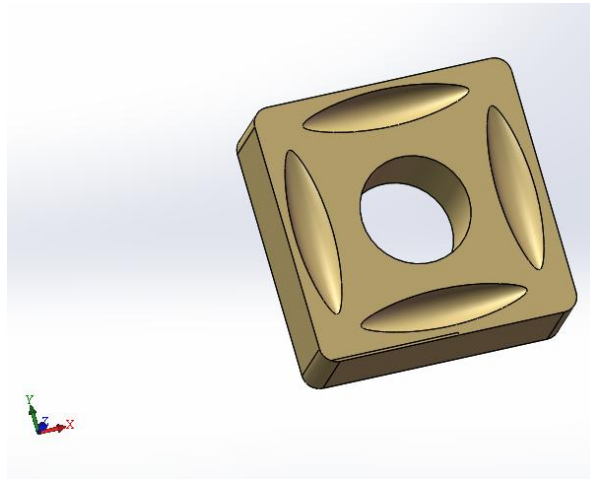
3D-модель ріжучої пластини фрези в SolidWorks
